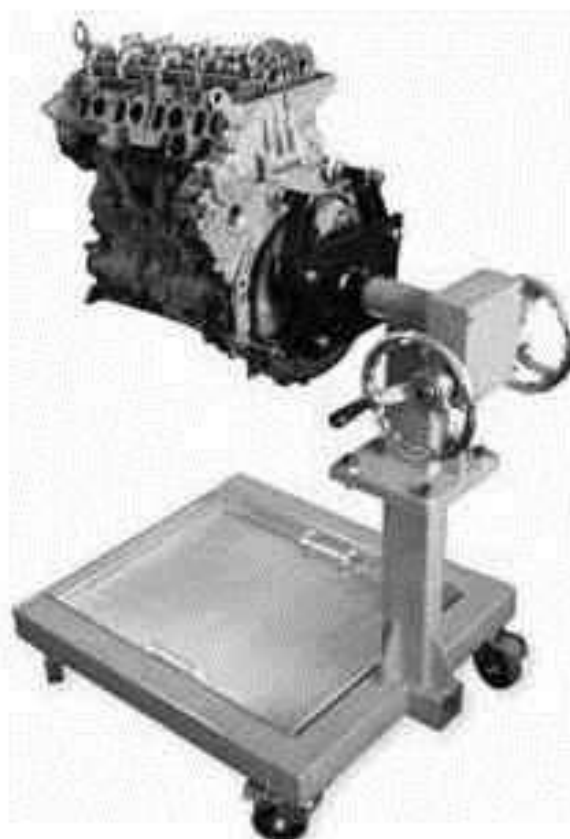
Универсальный кантователь для разборки узлов и агрегатов
